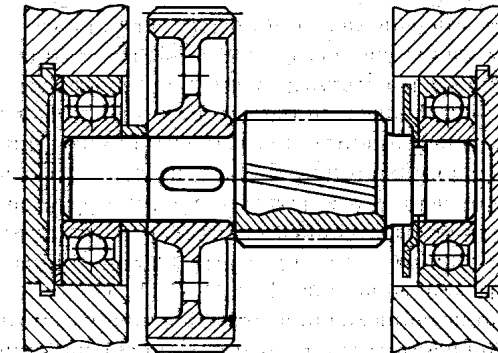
Промежуточный вал редуктора установлен на радиальных шарикоподшипниках; крышки врезные
